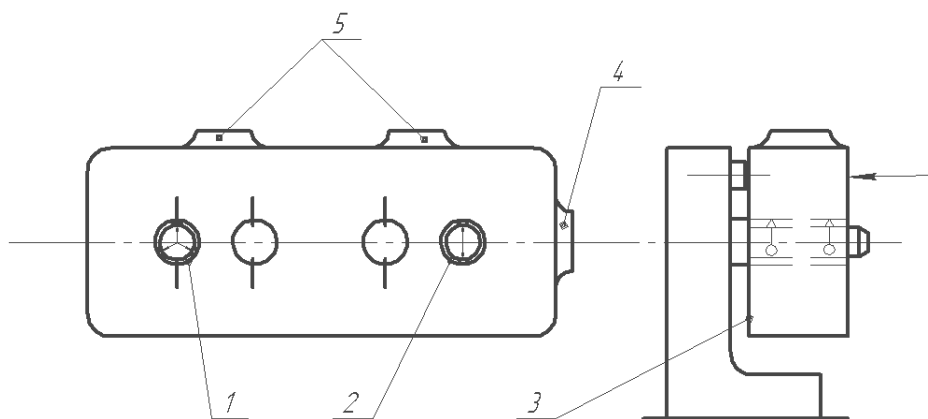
Базування корпуса з використанням консольних оправок
